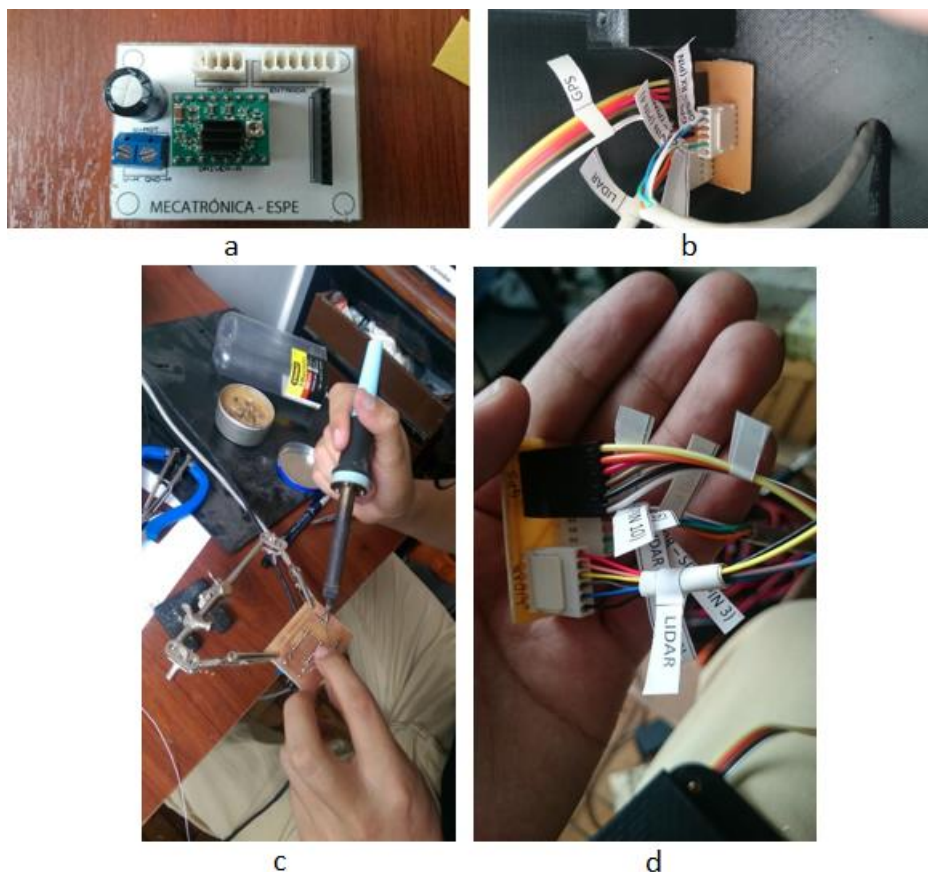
Armado y conexión de las placas de circuito electrónico; (a) placa de conexión, (b) placa Lidar, (c) soldadura y (d) etiquetado de cables.
